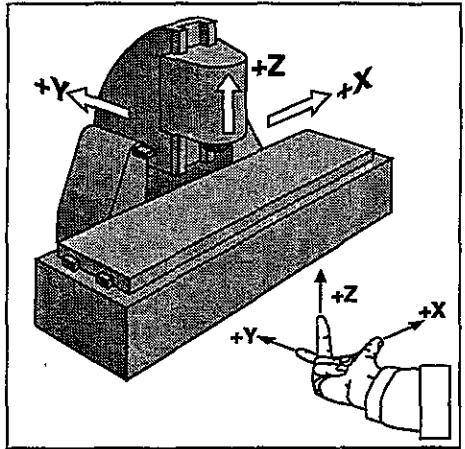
Désignation et sens des axes de la machine sur une fraiseuse
